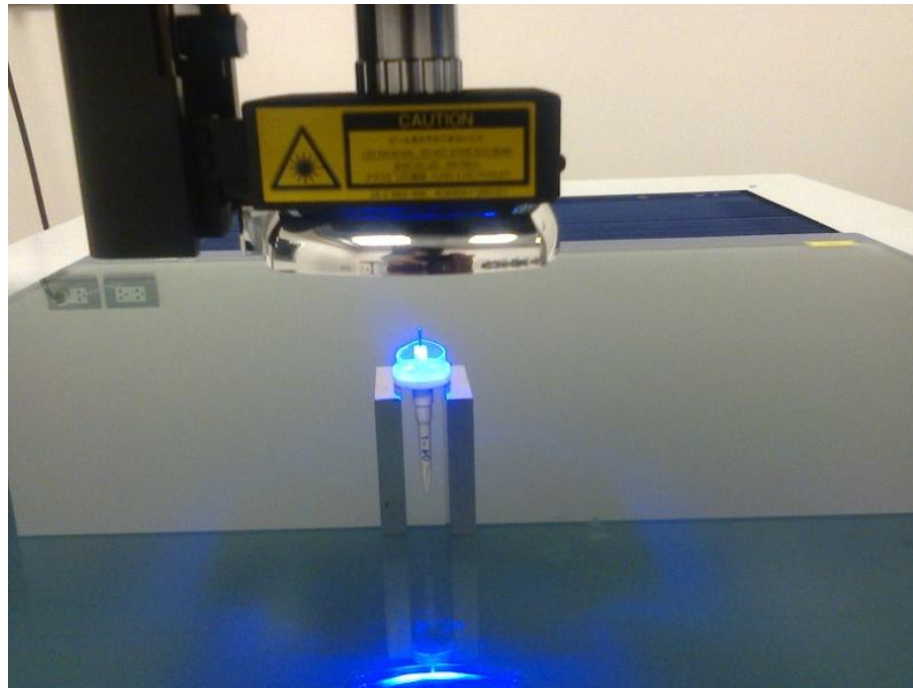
การแสดงผลของเครื่อง CNC Vision Measuring Machine สำหรับ IV Set 60 no.1
